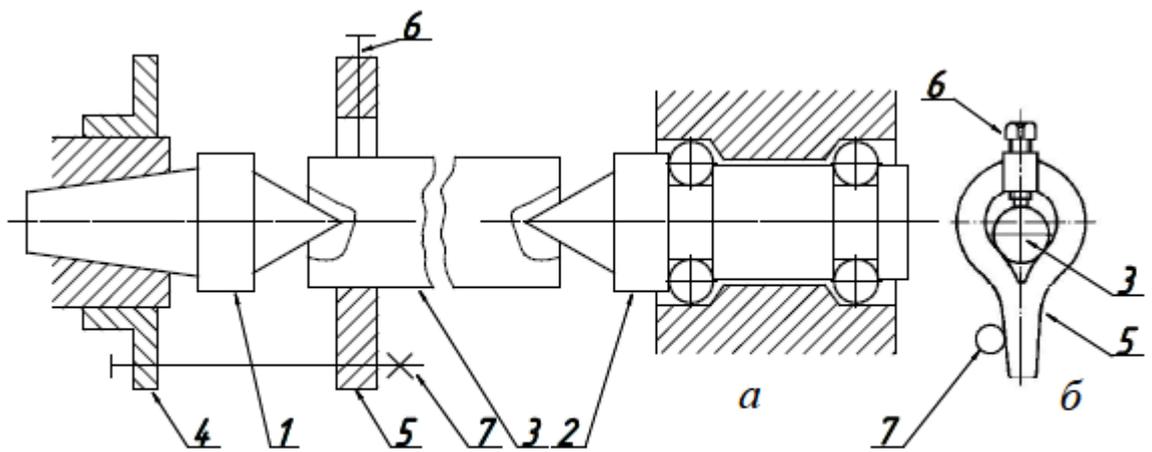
Схема установки вала в центрах с поводковым патроном на токарном станке
